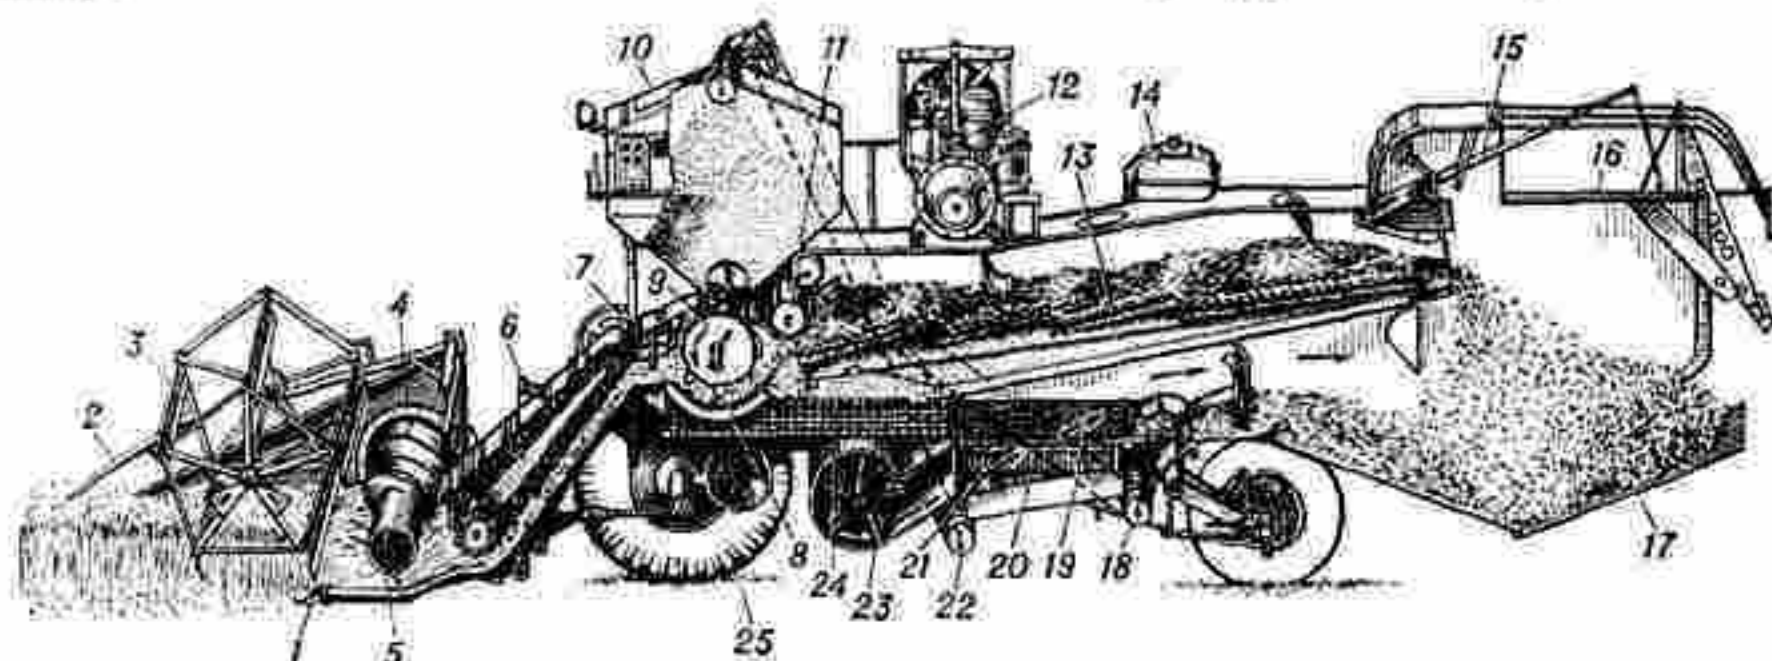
Устройство и технологическая схема комбайна: 1 — режущий аппарат; 2 — делители; 3 — мотовило; 4 — шнековый транспортер; 5 — пальчиковый механизм; 6 — наклонный транспортер; 7 — приёмный бите; 8 — подбарабанье; 9 — молотильный барабан; 10 — бункер; 11 — отбойный бите; 12 — двигатель; 13 — соломотряс; 14 — топливный бак; 15 — соломоуловитель; 16 — копнител; 17 — откидное днище копнителя; 18 — колосовой шнек; 19 — верхнее решето очистки; 20 — нижнее решето очистки; 21 — скатная доска; 22 — шнековый зерновой транспортер; 23 — вентилятор; 24 — транспортная доска; 25 — ведущее колесо.
